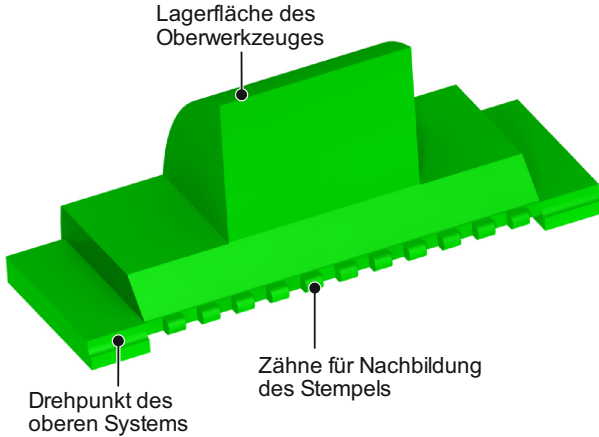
Führung der Oberwerkzeuge über eine Verzahnung und einer außenliegenden Führung
